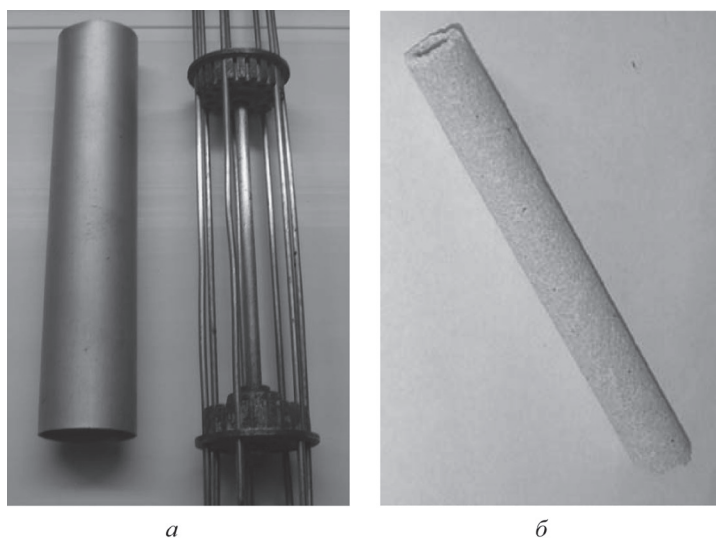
Оснастка для формирования КС: а) корпус из АМг, крышки в сборе со спицами; б) крупнопористая вставка из порошка фарфора [16]
